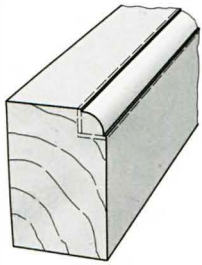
Сначала обрабатывают фрезой рёбра, а затем с помощью дисковой пилы вырезают фальцы: 1 — брусок обвязки; 2 — штапик.
